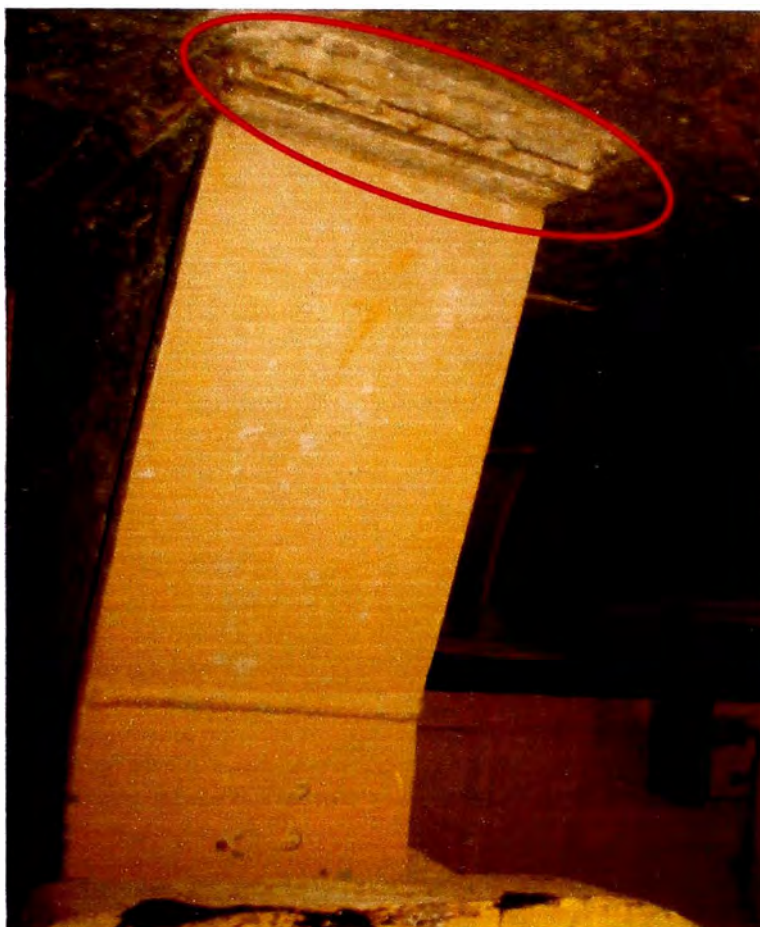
Fisura en el guiador de tolva.
